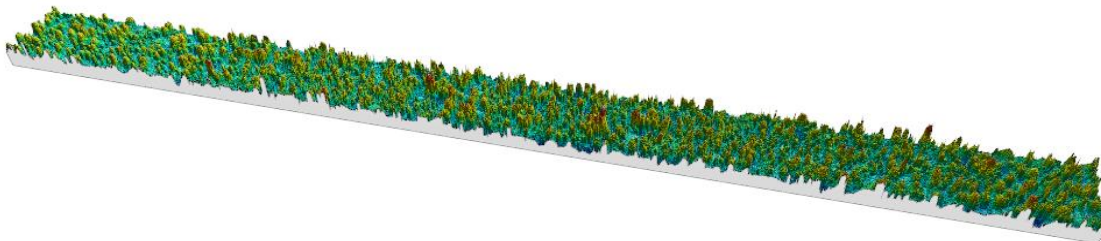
3D zobrazení vyhodnocovaného povrchu po úpravě dat, základní povrch
